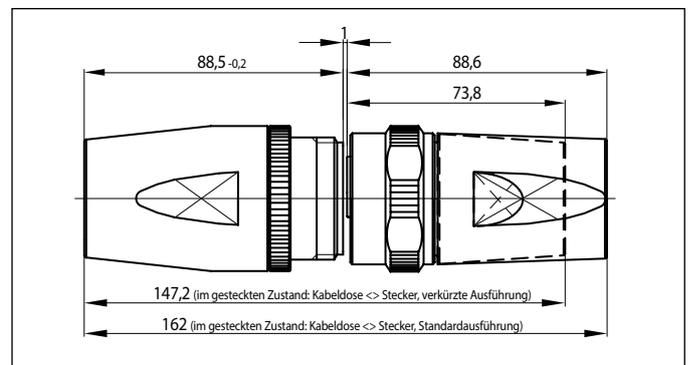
Einbaumaße und Maße im gesteckten Zustand für die Kombination Kabeldose und Kabelstecker in Standardausführung sowie Kabeldose und Kabelstecker in verkürzter Ausführung
